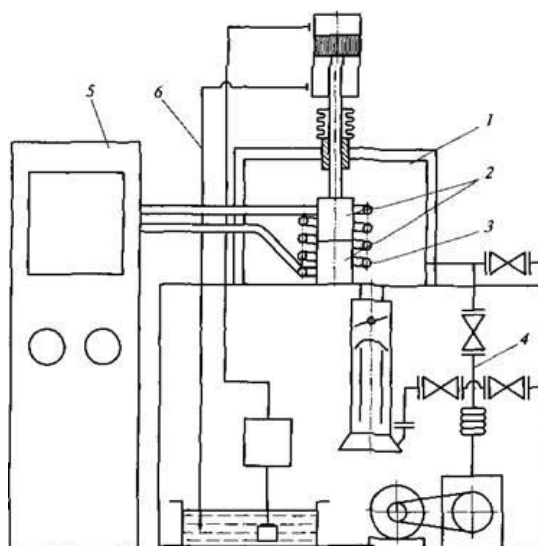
Принципиальная схема машины для диффузионной сварки МДВ-301 94
